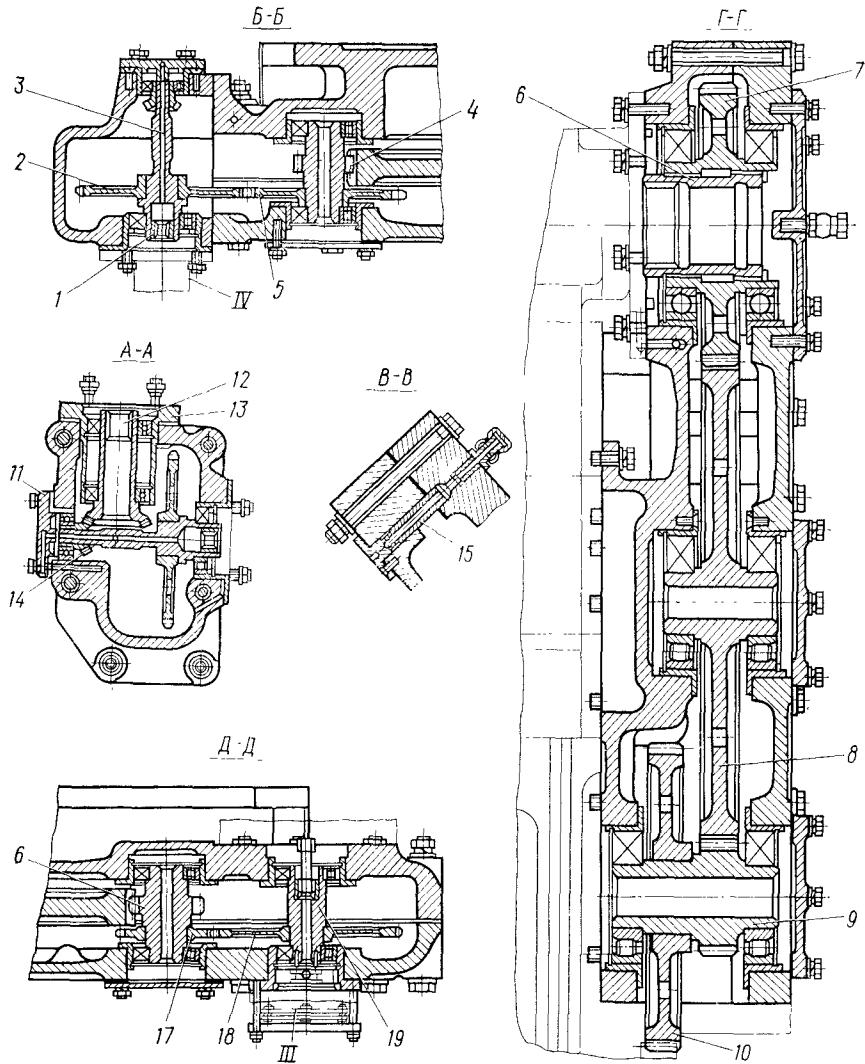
Привод распределительного вала восьмицилиндрового дизеля:
